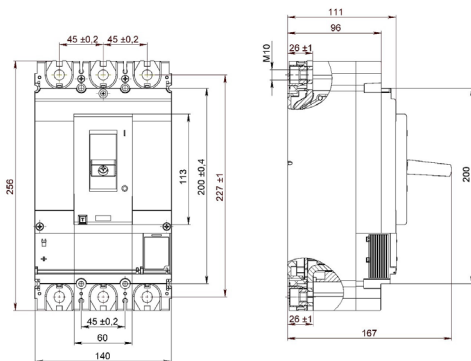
Габаритные, установочные и присоединительные размеры выключателей
